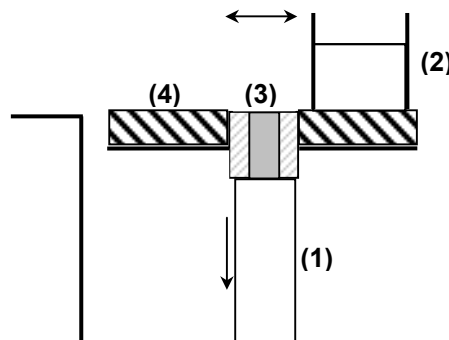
Remplacement de la cuve par un piston amovible [Hinczewski et al., 1998 ; Licciulli et al., 2005] ; (1) piston amovible ; (2) container ; (3) objet en construction ; (4) plaque de verre.
